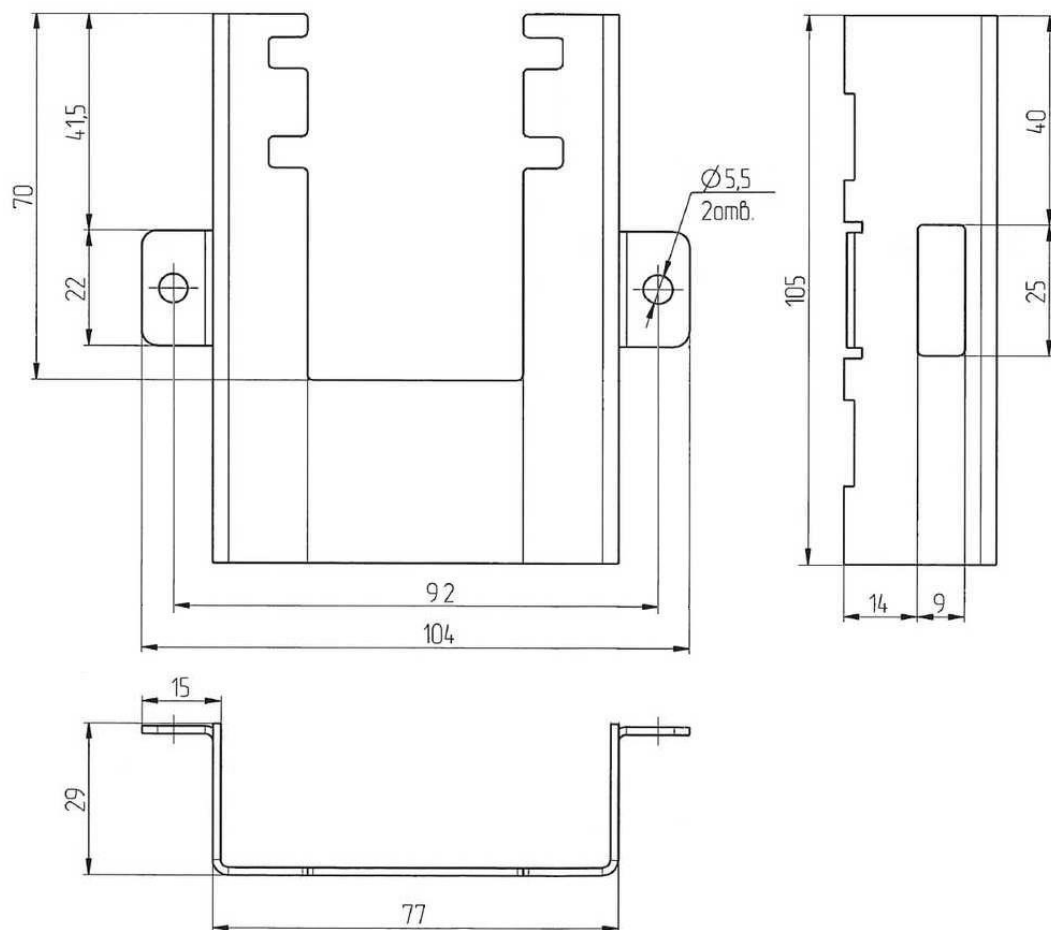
Внешний вид, габаритные и установочные размеры кронштейна M15.034.08.002
